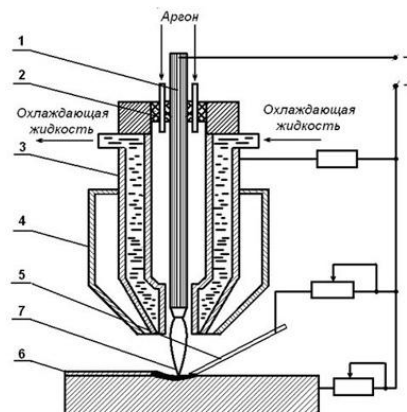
Схема плазменной наплавки токоведущей проволокой.
